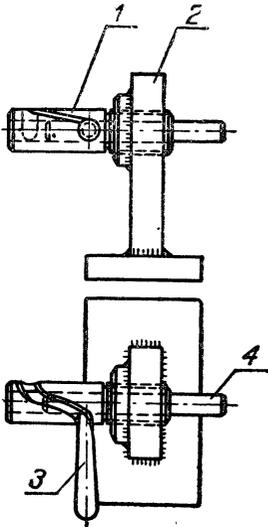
Зажим для зажатия отбортованных деталей при сборке.
